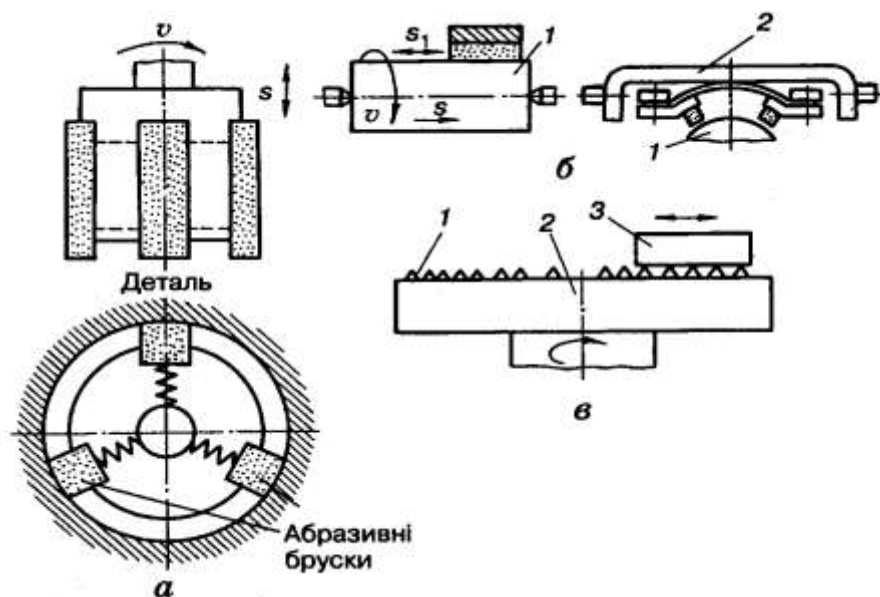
Схеми чистової обробки поверхонь деталей машин
